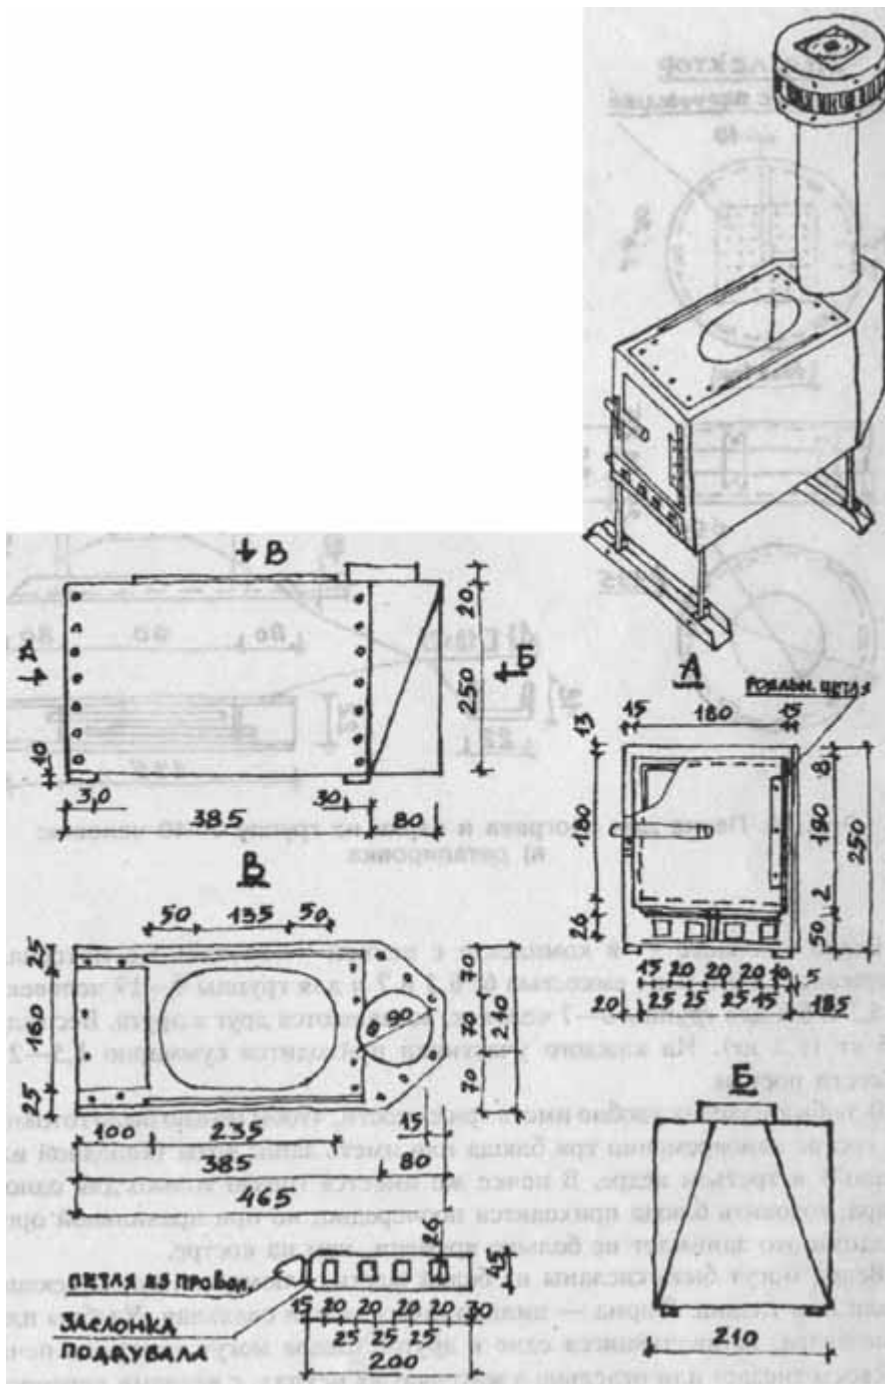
Печка для обогрева и варки на группу 6—10 человек: а) общий вид; б) вид и размеры в трех проекциях
